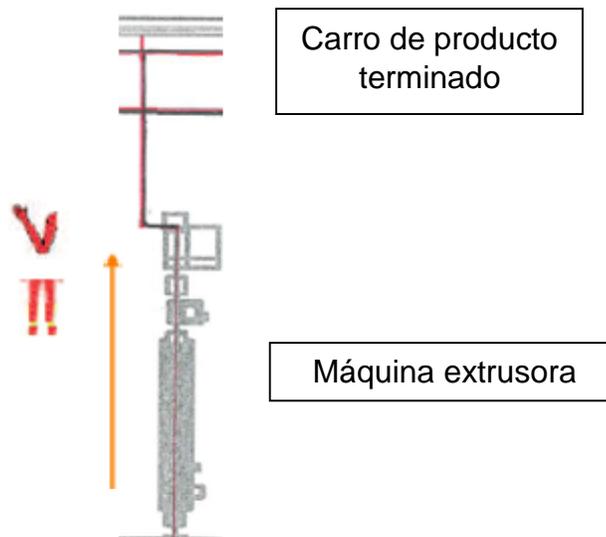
Máquina extrusora y carro de producto terminado en el área 1.
